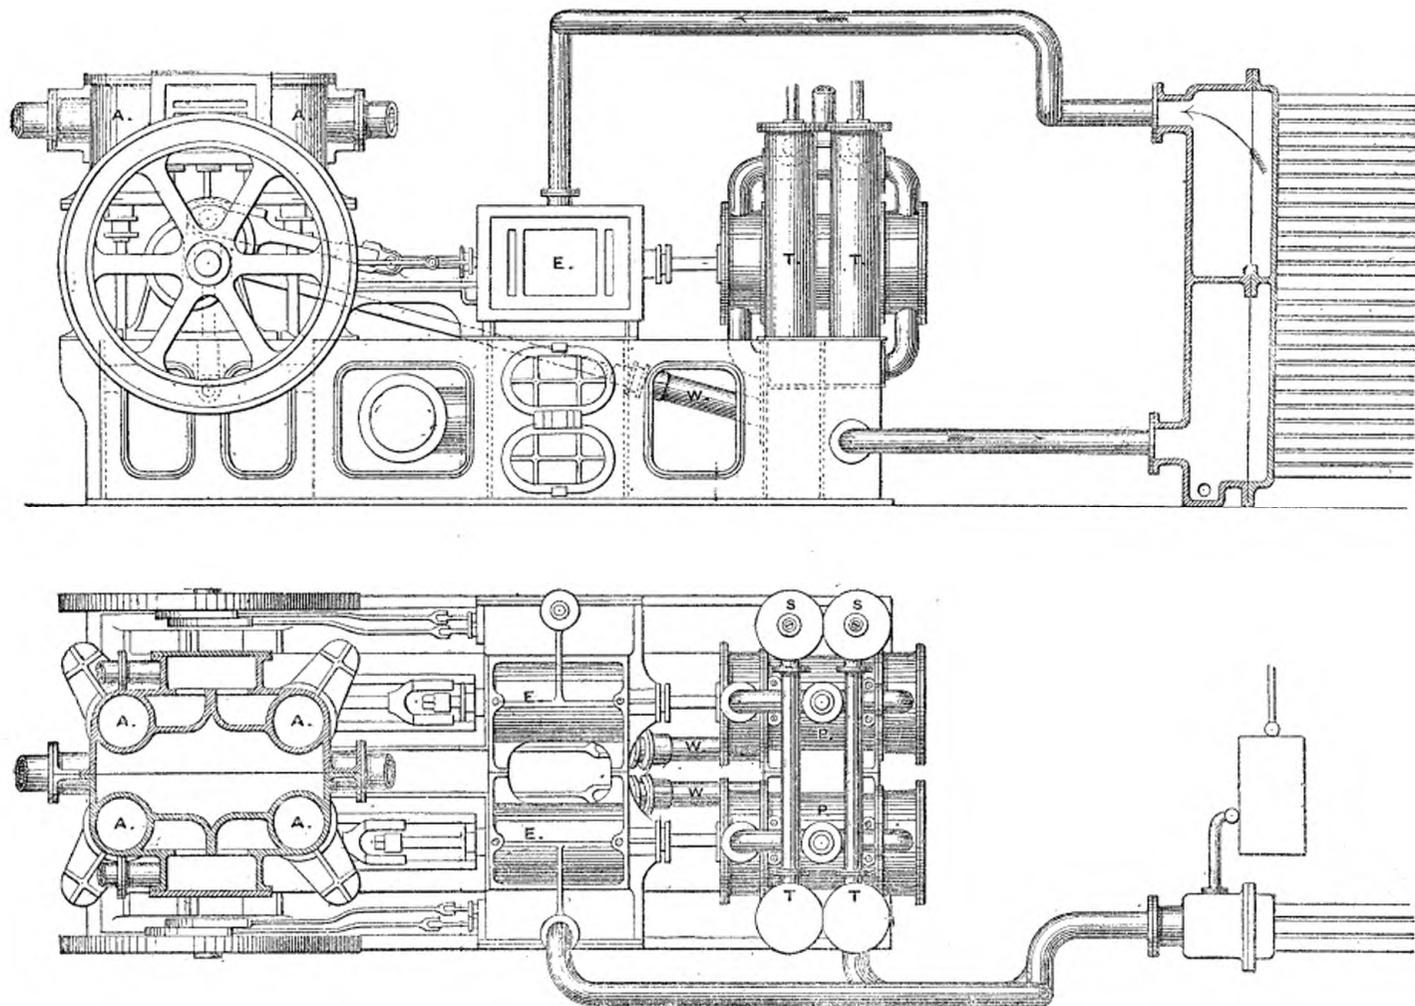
et 147. — Bell-Coleman, Machine de 1879, type marin.
